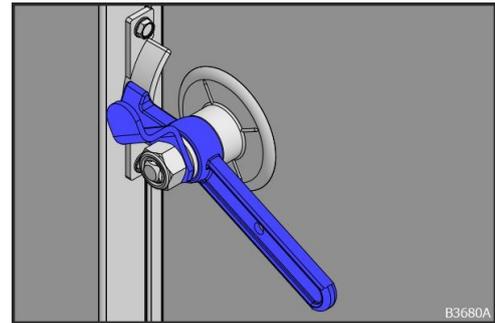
Nockenzunge mit Innenhebel und Fanghaken (druckseitig)
